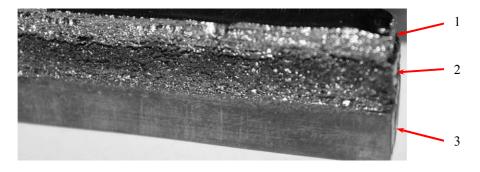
Образец изделия, изготовленный методом электронно-лучевой 3D-наплавки: 1- верхний слой наплавленного металла; 2- промежуточный слой металла с частицами нерасплавленного порошка; 3 – подложка из титана
